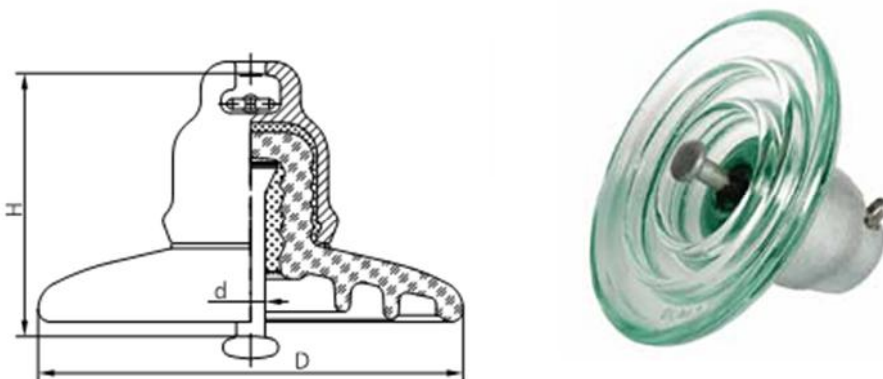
Principales dimensions et forme de l'isolateur U 40B [22].
